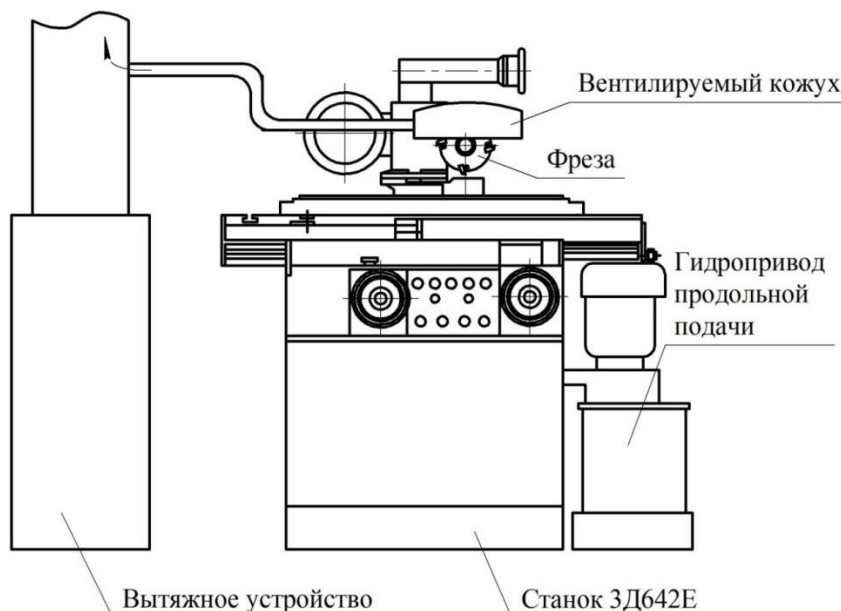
Экспериментальный стенд на базе станка ЗД642Е, модернизированный под процессы фрезерной обработки
